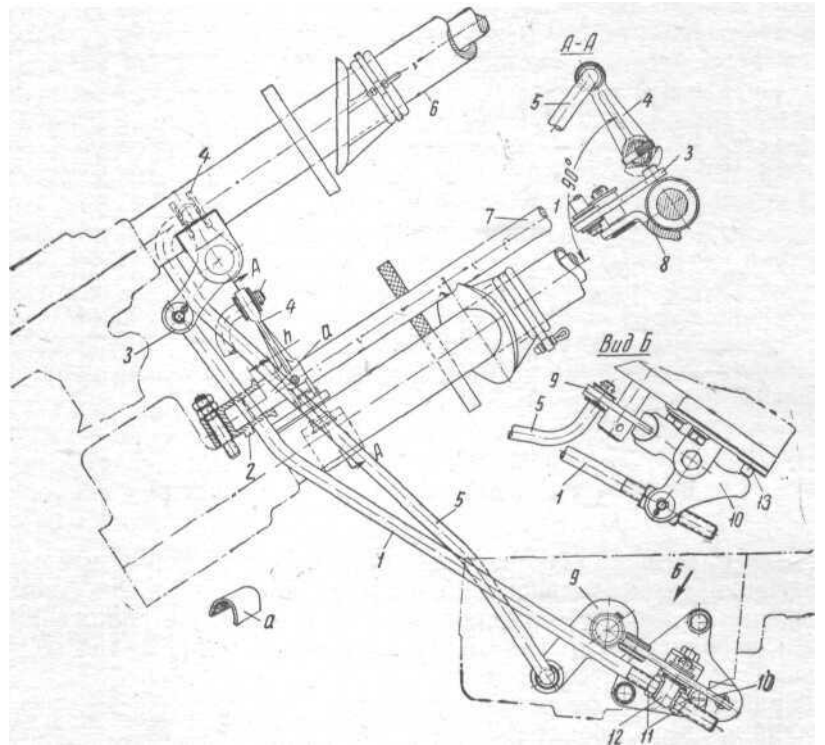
Механизм привода управления коробкой передач модели 407:
